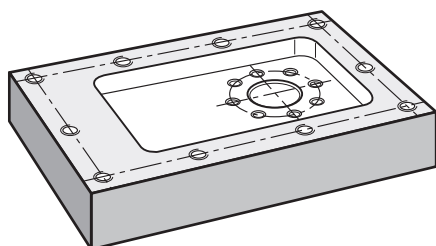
Образцовая деталь – Изготовление отверстий на окружности и ряда из отверстий
